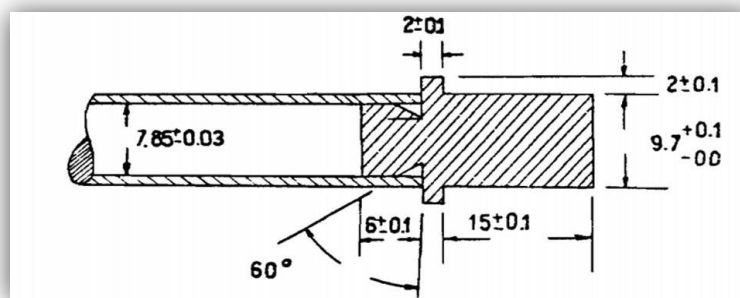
Diseño de junta para la soldadura del tapón de las barras. Medidas en mm.
